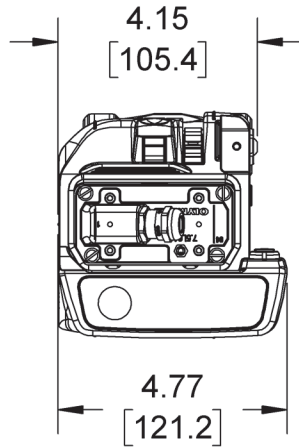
Dimensioni della vista superiore dell'HydroFORM senza encoder dell'indice
